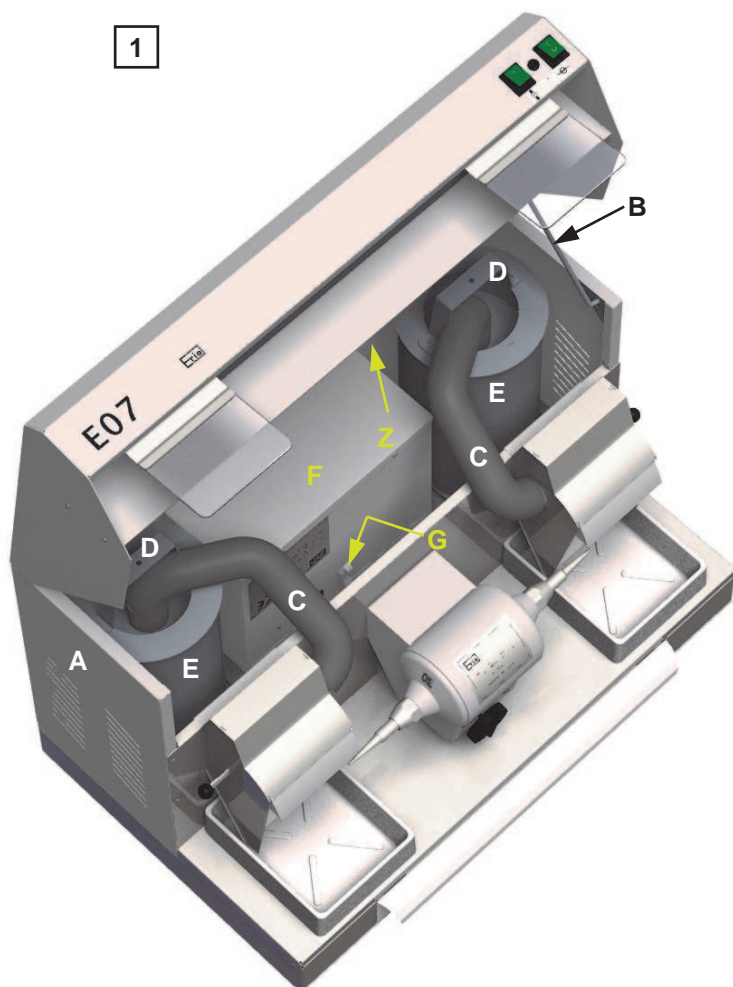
Sollevare il coperchio dell'apparecchio (A) ed assicurare la sua apertura tramite l'asta B. Sfilare il tubo flessibile (C) dall'imbocco. Estrarre il telaio porta filtro (D) dalla camera di aspirazione (E), sollevandolo.
